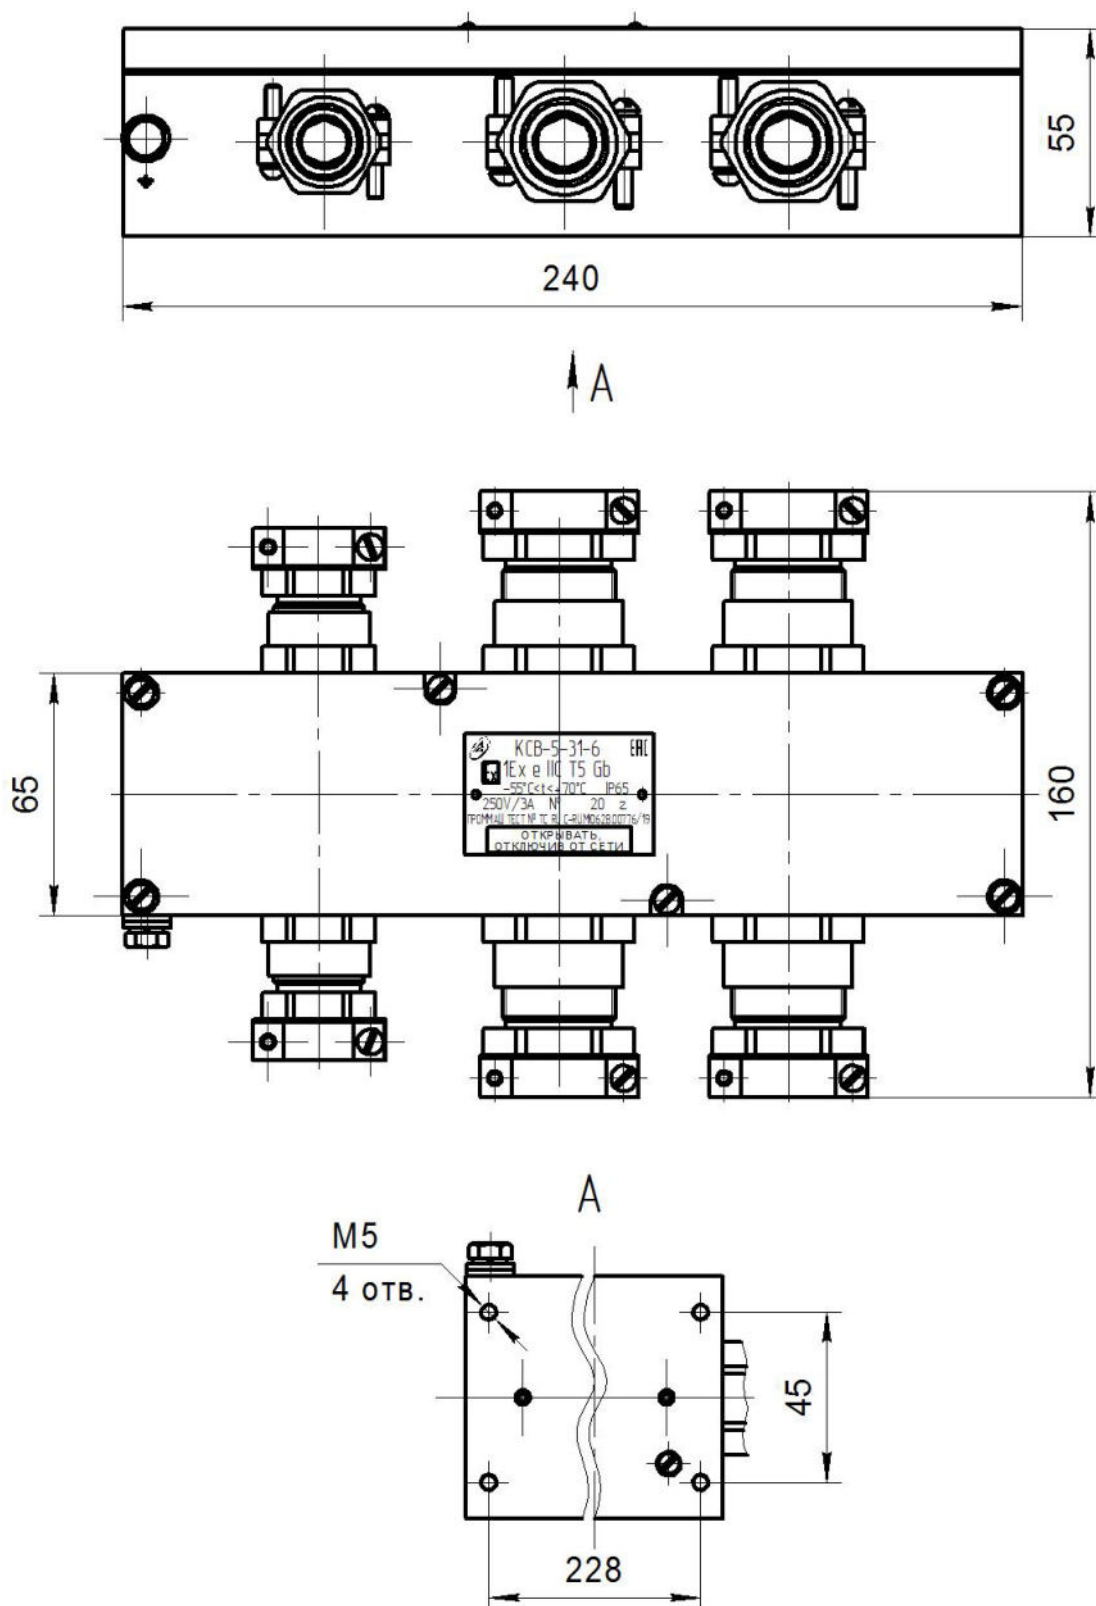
Внешний вид и соединительные размеры коробки КCB-5-31-6
